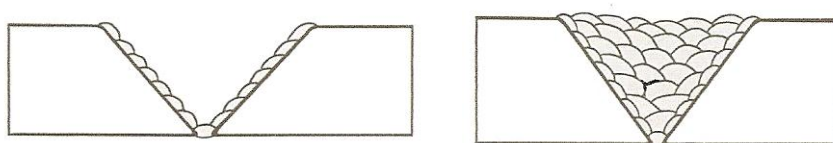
Técnica de estanhagem (à esquerda) e técnica de estanhagem com soldadura em múltiplas passadas (à direita)
